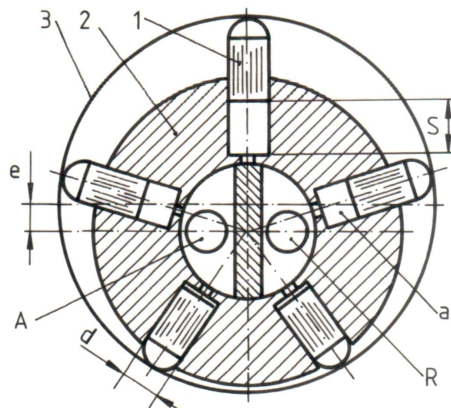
Pompă cu pistonăse radiale: 1 - pistonăse; 2 - rotor; 3 - stator; 4 - placă fixă; a - cameră de pompare; A - canal de aspirație; R - canal de refulare
